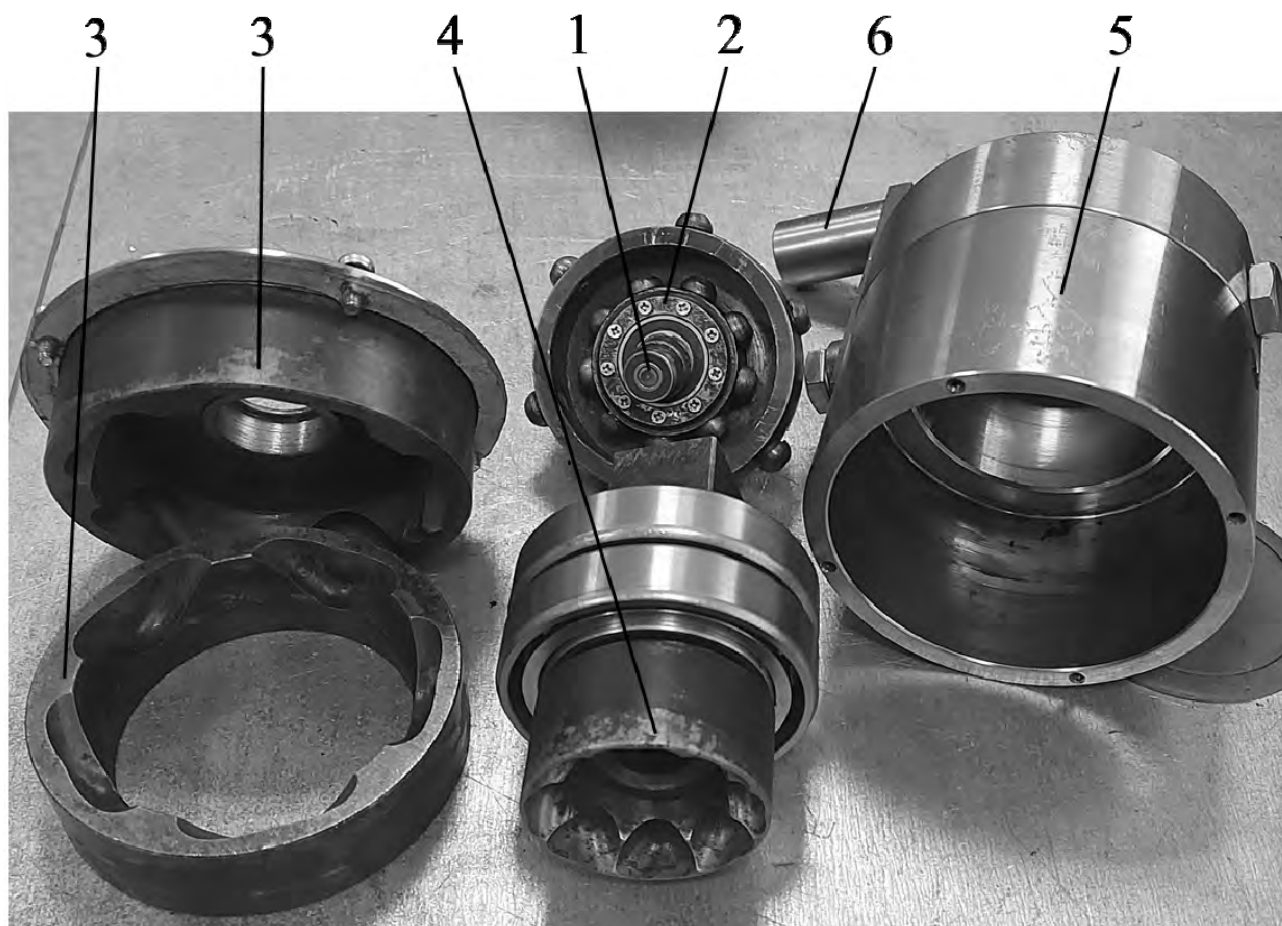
Общий вид мотор-редуктора с СРП
